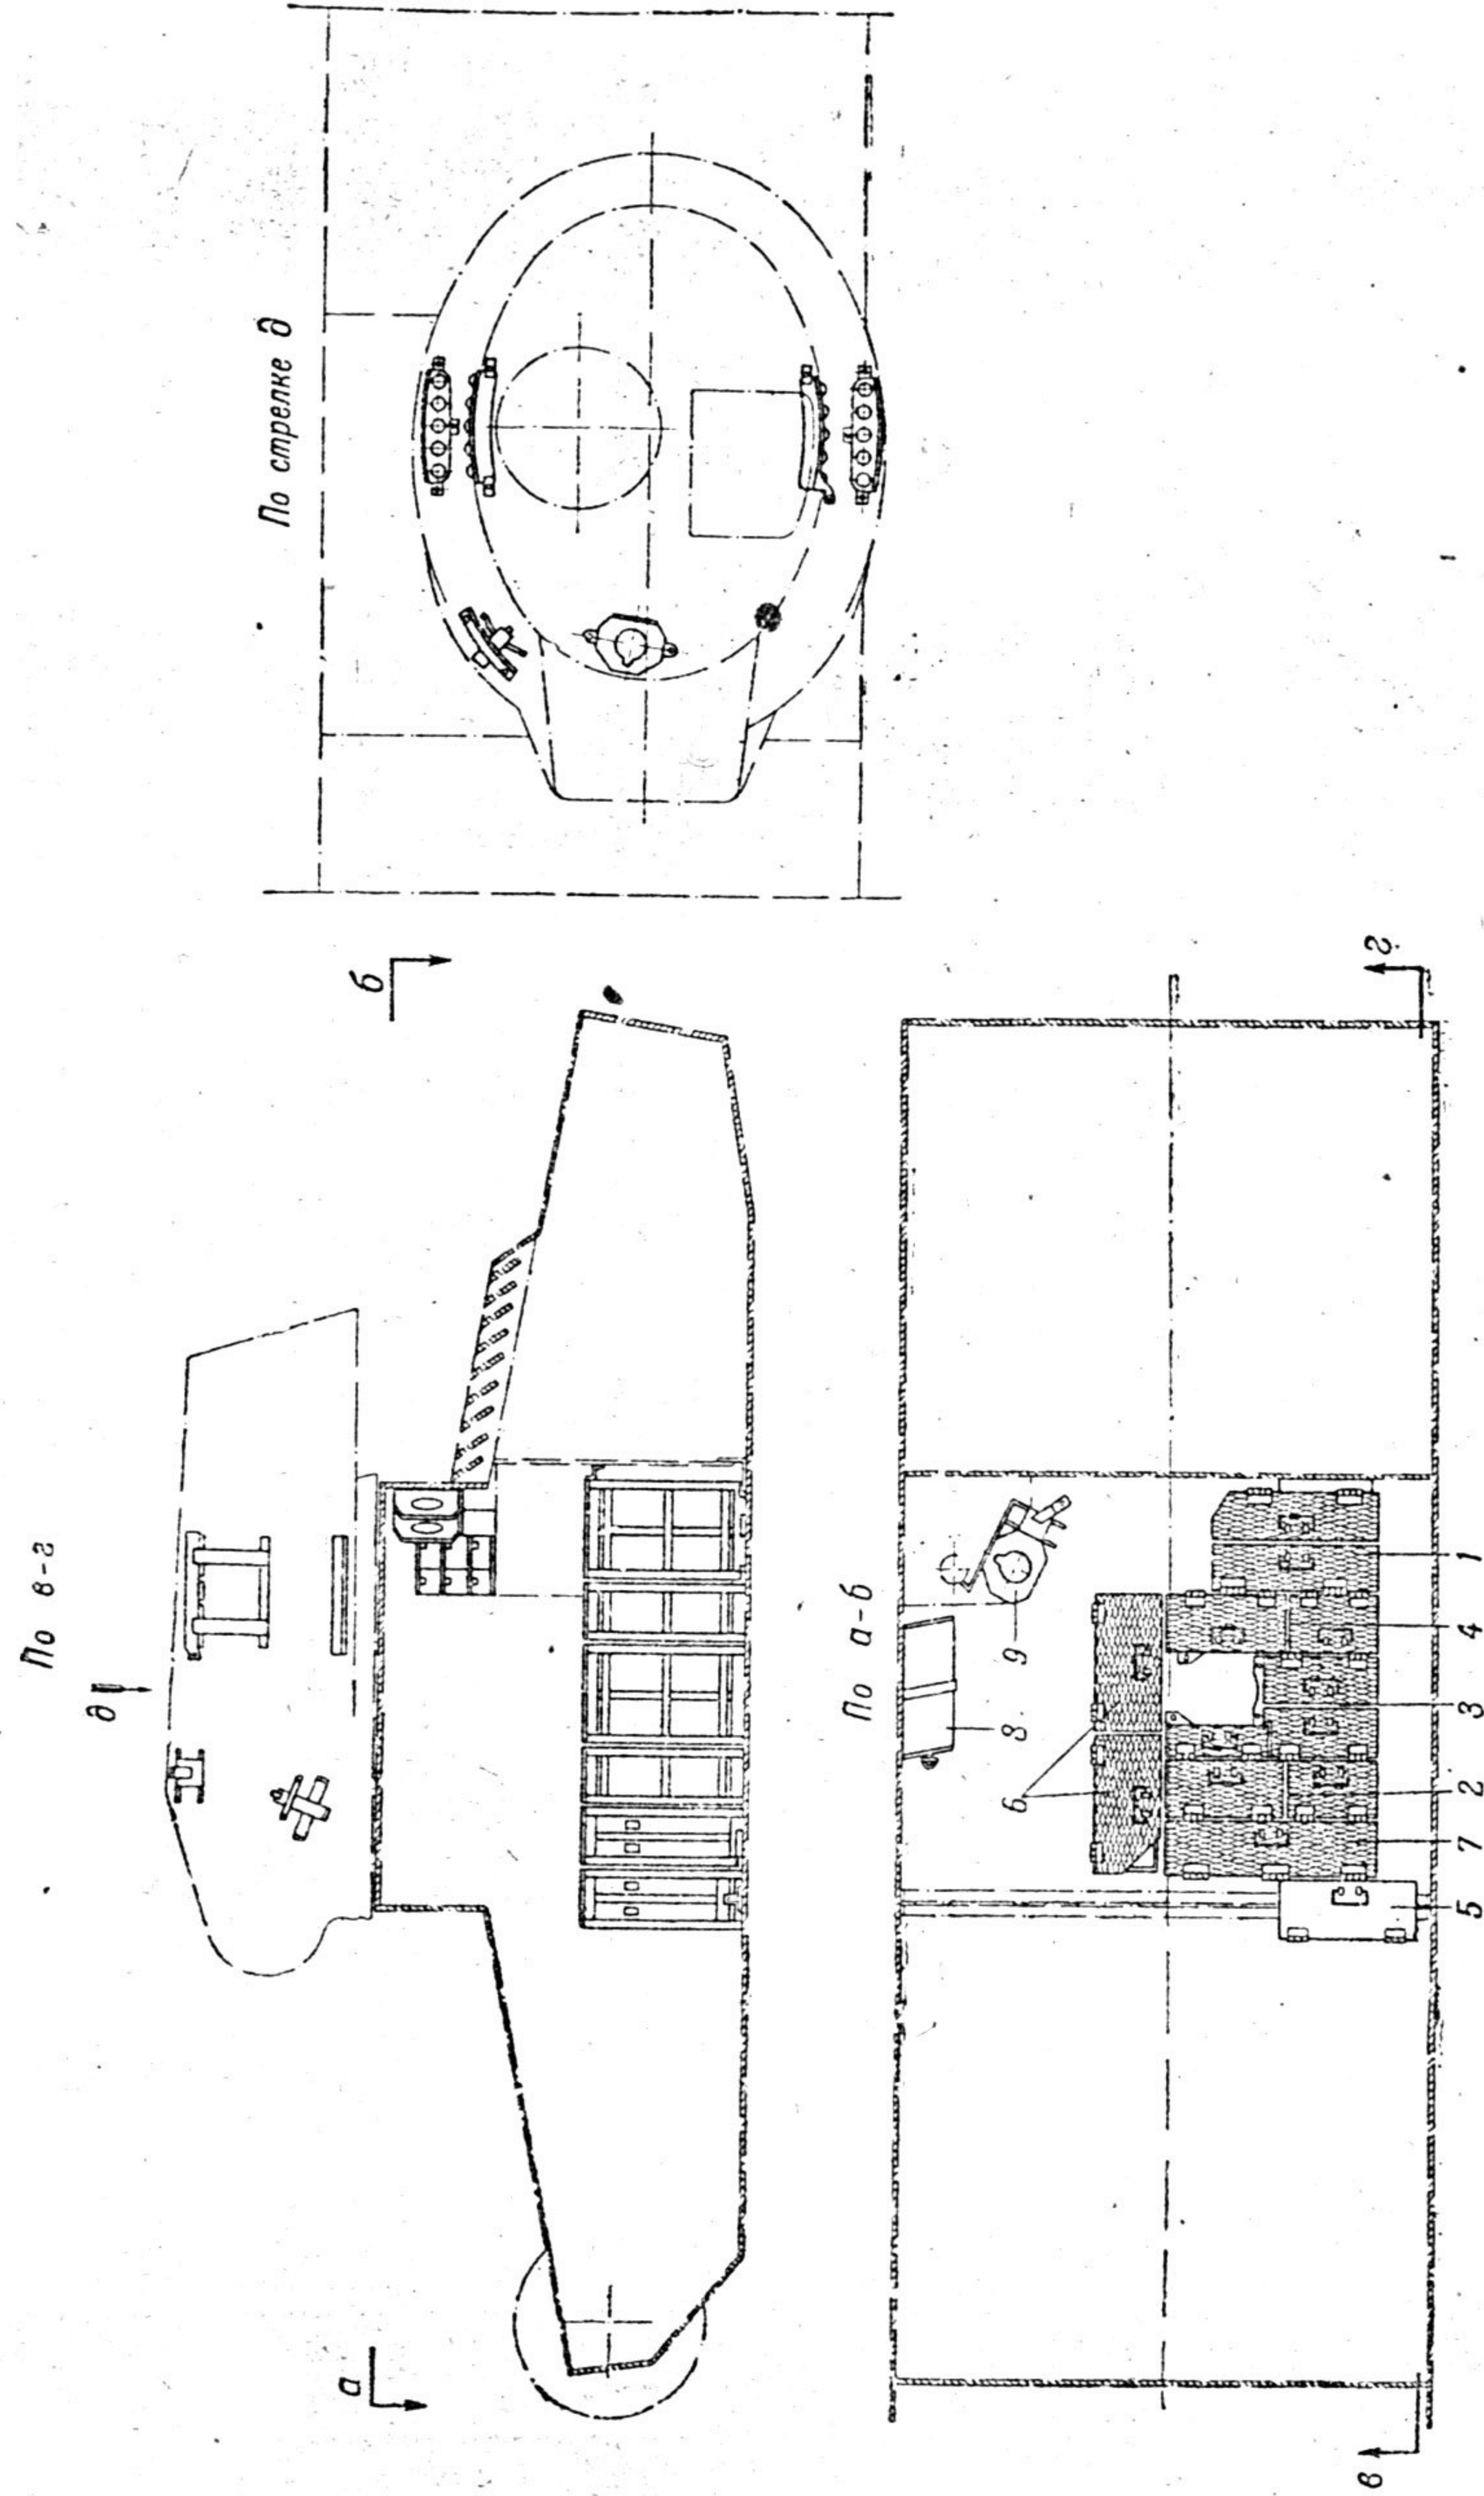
Укладка боеприпасов в корпусе с прямой подбашенной коробкой:
